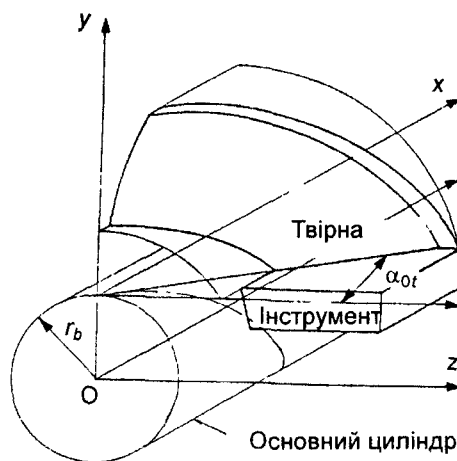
Профіль I — Метод механічного оброблення різцем
